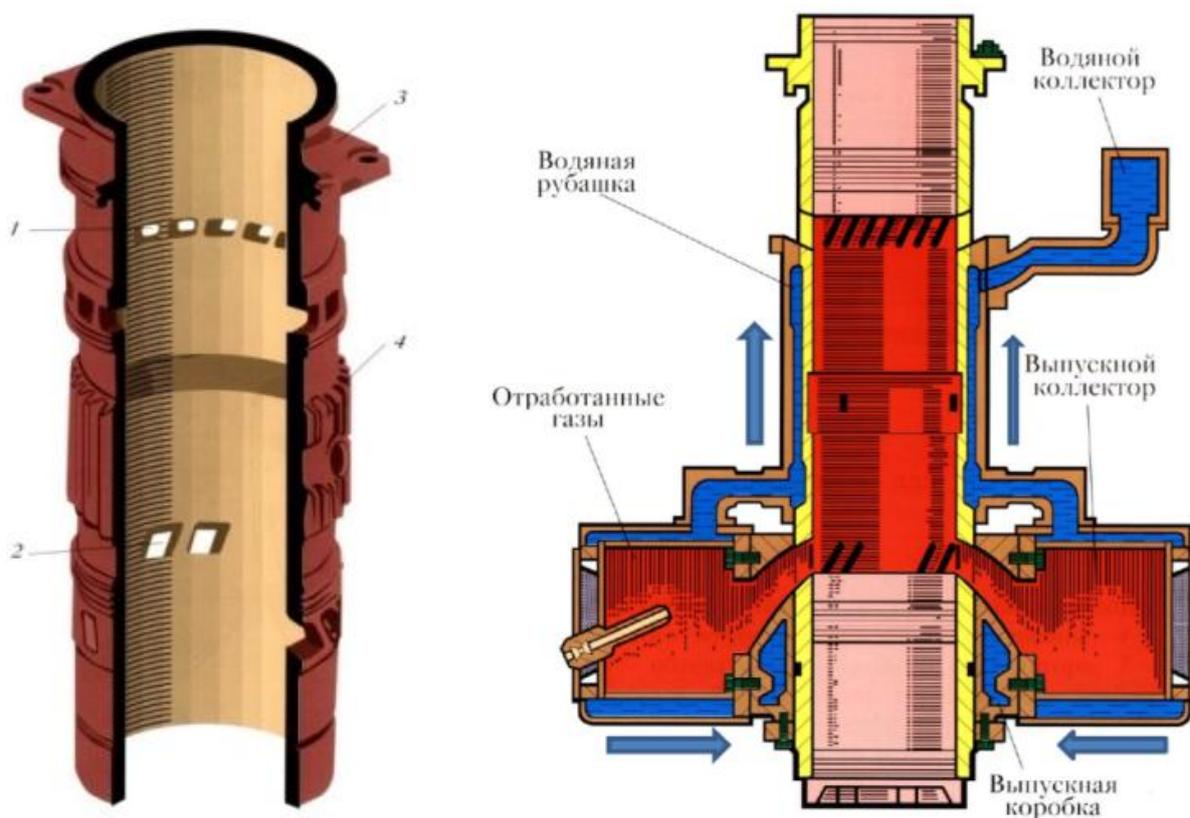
Цилиндровая втулка дизеля 10Д100
